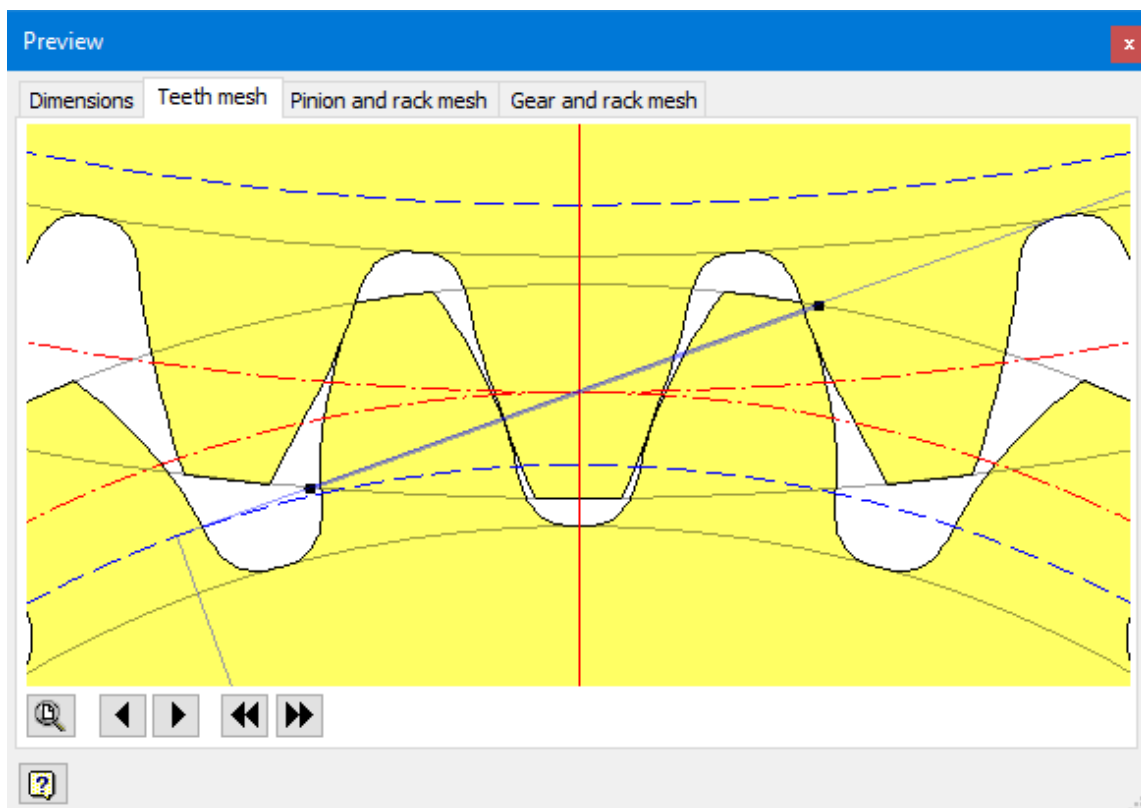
Двовимірний кресленик зубчастого циліндричного зачеплення
